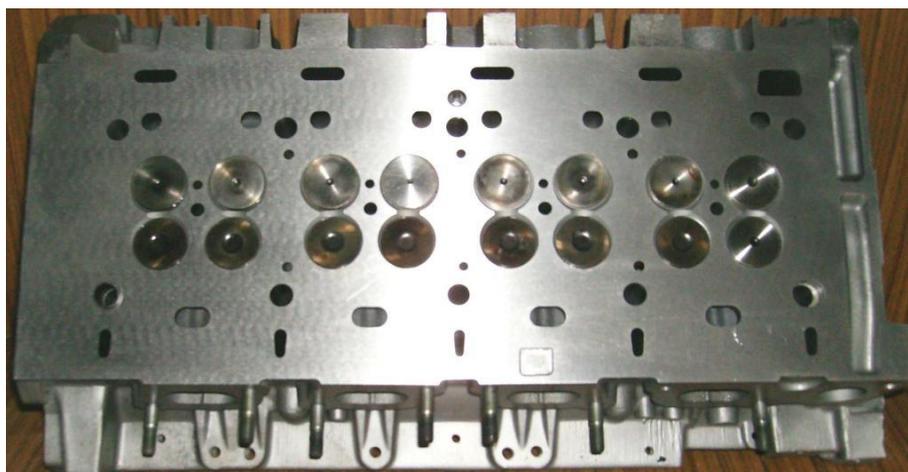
Общий вид головки блока цилиндров после устранения трещин ГДН, механической обработки [7,с.272] и сборки
